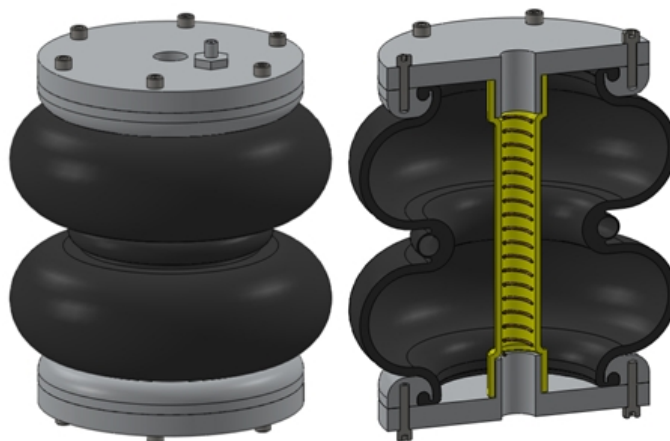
Desenho e corte 3D do protótipo da mola de gás.
